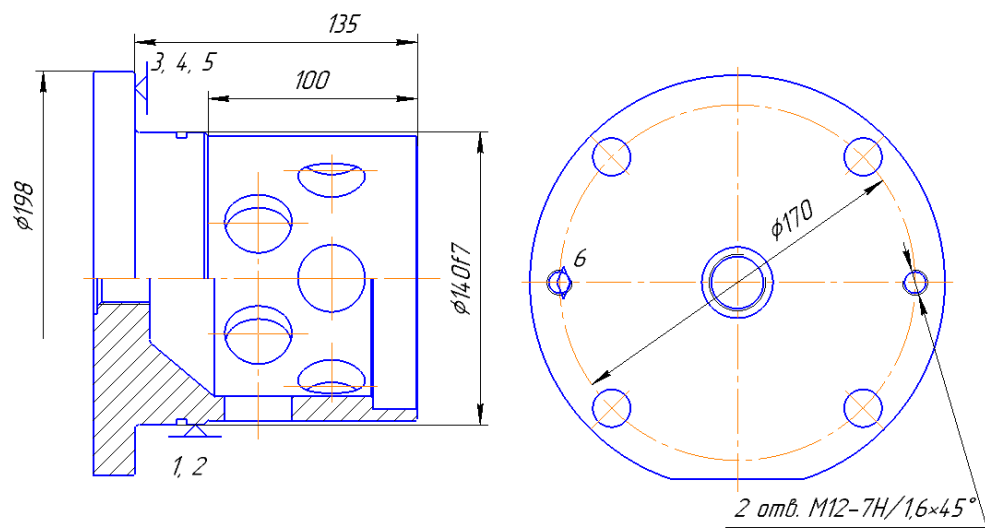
Схема базування деталі Ліхтар 4ГМ2.5-02.06 у виробі
